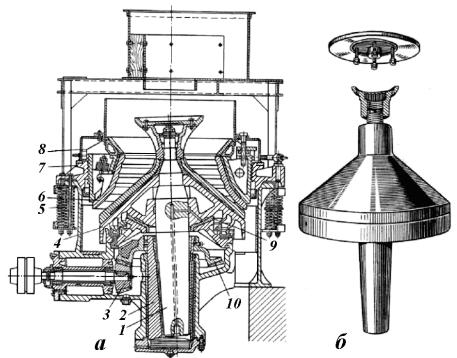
Конусная дробилка с пологим конусом: a – разрез; δ – конструкция дробящего конуса на консольном валу
